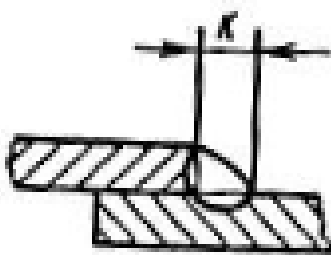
Конструктивные элементы сварочного шва, согласно ГОСТ 14771-76.
